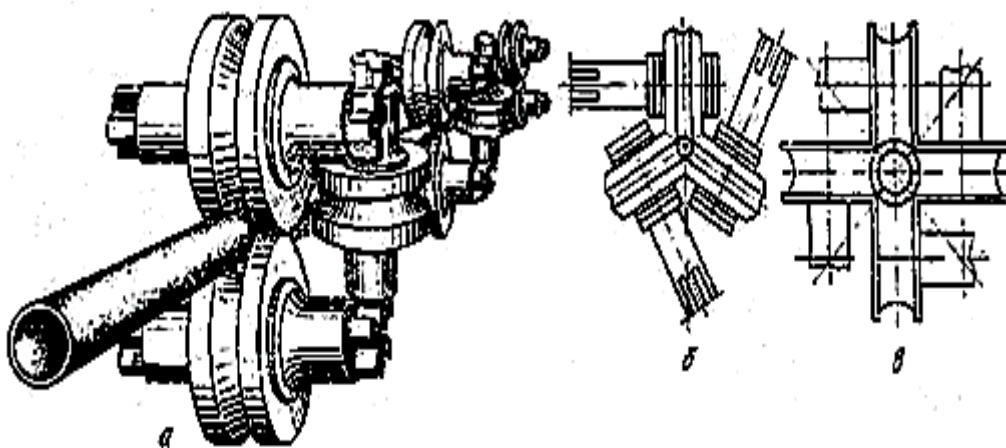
Калибровочный (редукционный) стан трубопрокатного агрегата 110 [11]
